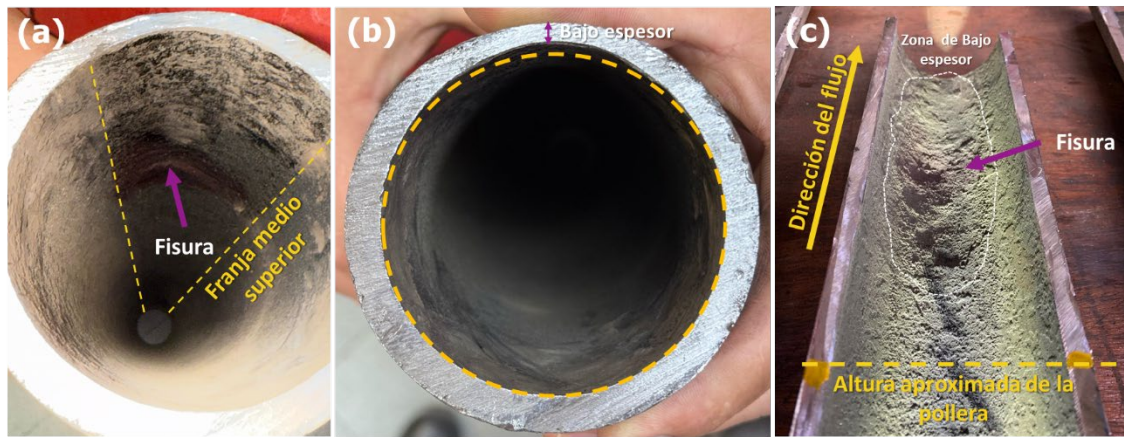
Inspección visual interna del tramo de tubo reemplazado. (a) Franja interior y ubicación de la fisura. (b) Bajo espesor en la sección transversal del tubo, coincidente con la ubicación de la franja. (c) Ubicación de la zona de bajo espesor y fisura que originó la falla en la mitad superior del tubo. Se indica la altura aproximada de la protección a la llama.
